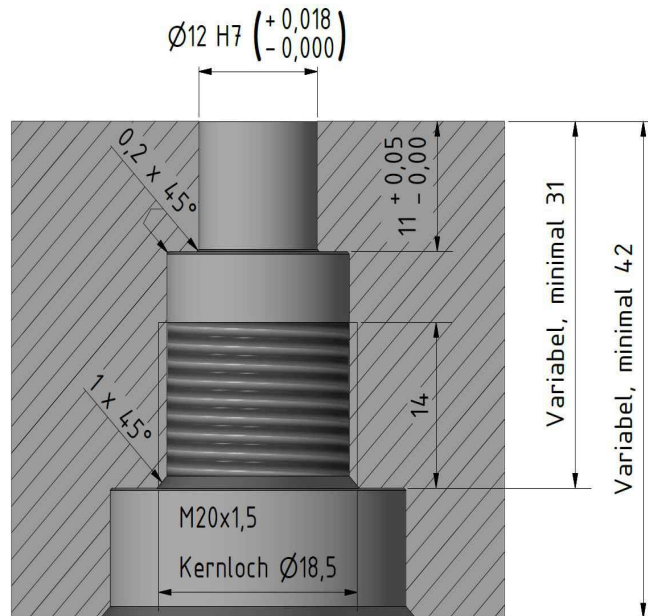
Gestaltungsvorschlag Sensoreinsatz im Werkzeug
